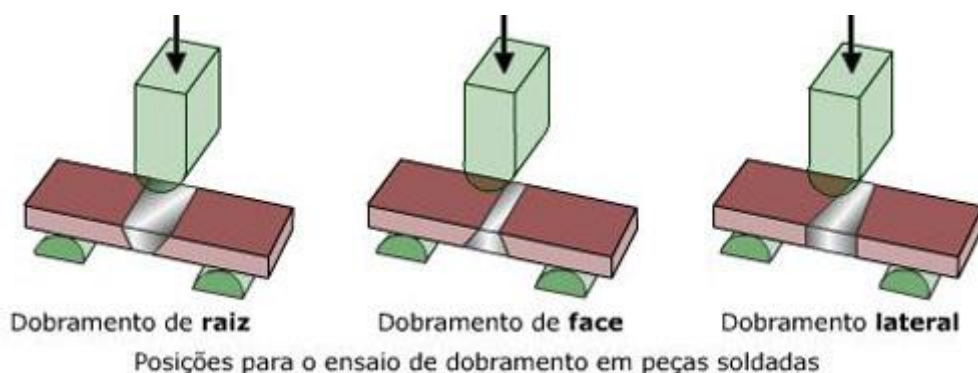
Posição dos ensaios de dobramento . Disponível no site CIMM.
